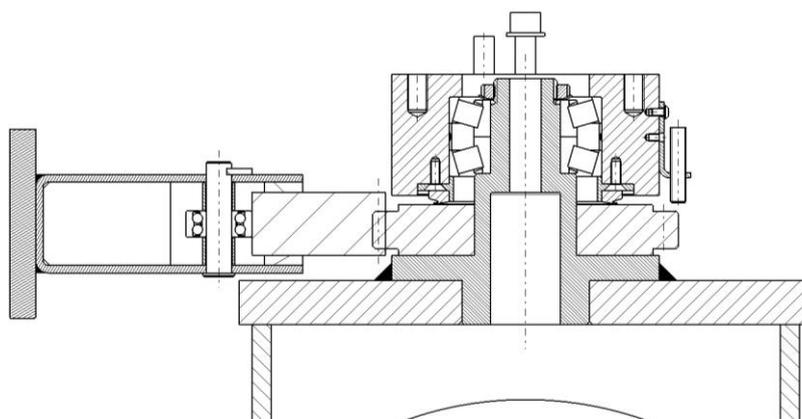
Detalle del montaje del piñón-cremallera con su rodamiento, el sensor de lectura del piñón y el montaje del rodamiento principal de la dirección.
